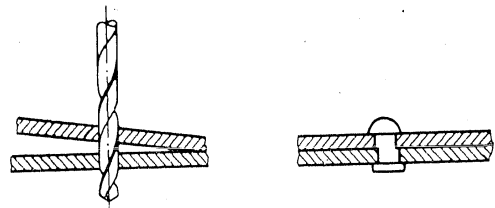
Schlecht gebohrt; abgesetzter Nietschaft
